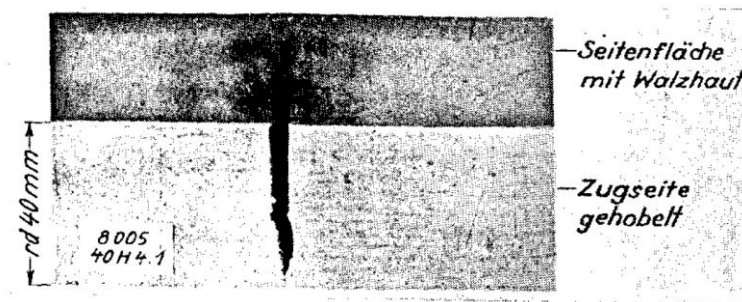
Probekörper mit Ermüdungsriss an der Seitenfläche mit Walzhaut #250
